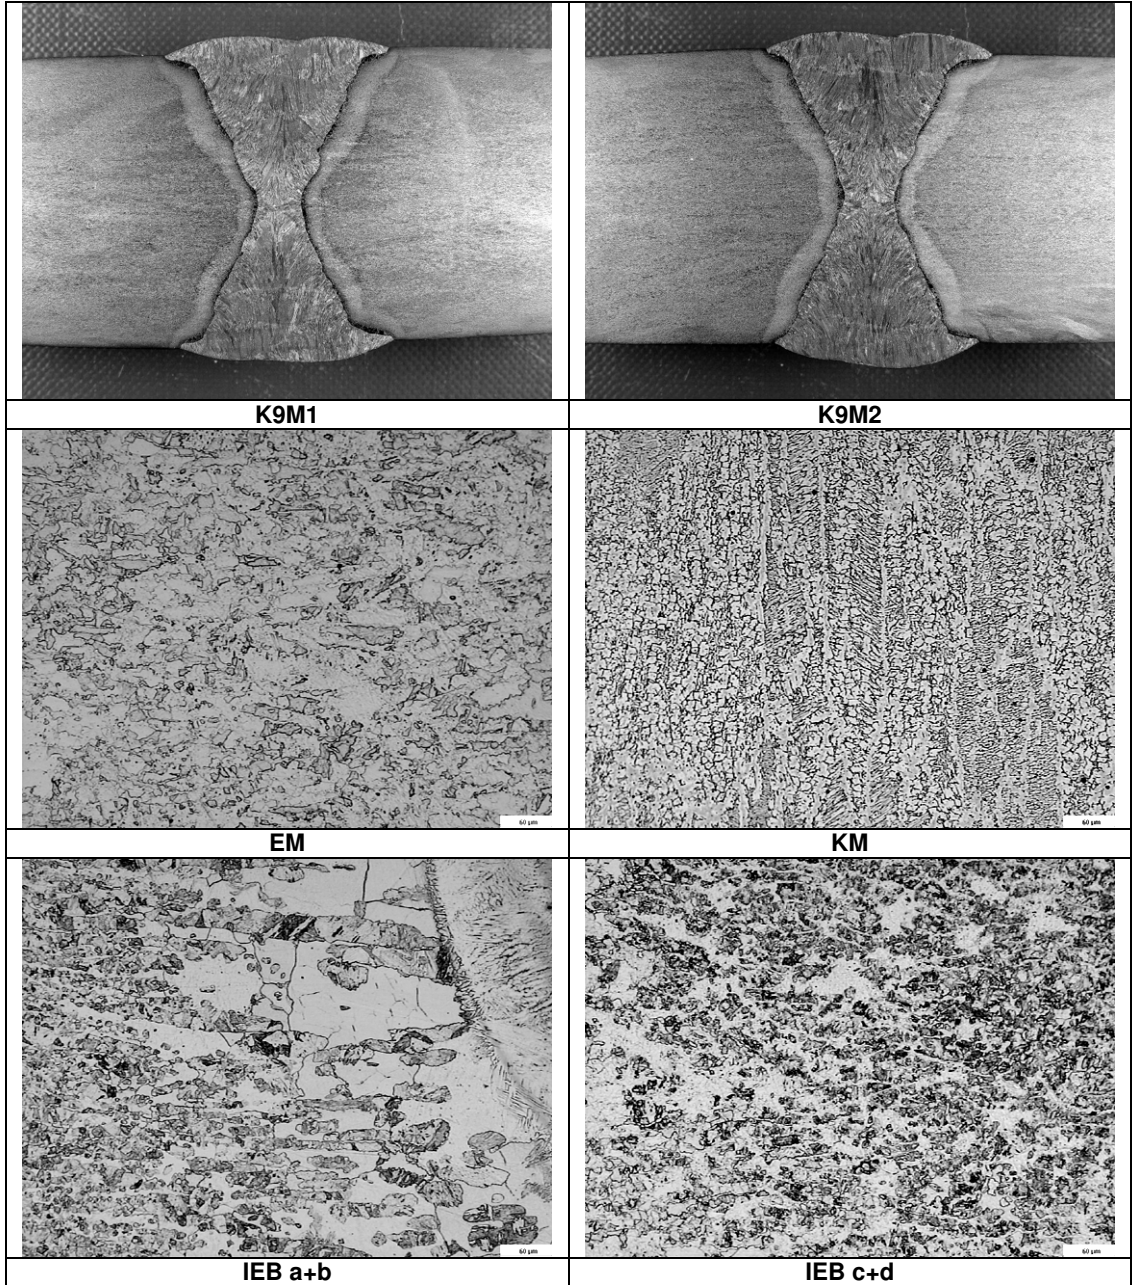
20 mm kalınlığında 309 tür ek metal ile FCAW kaynaklı bağlantının makro ve mikroyapıları (F9).
